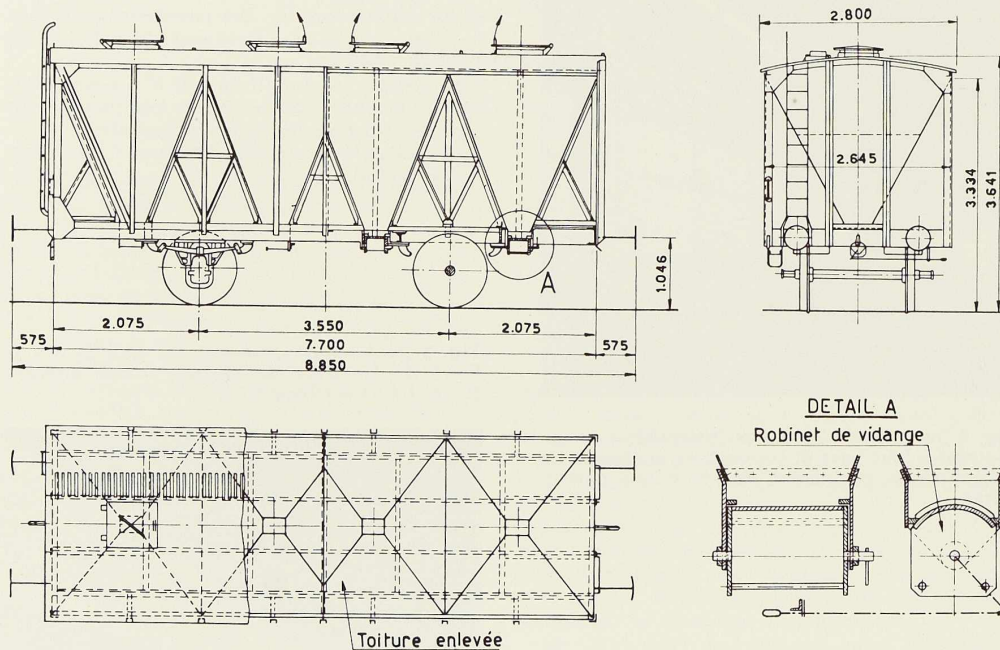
Elévation, vue en plan et coupe d'un wagon-trémie pour le transport du ciment en vrac, en service à la S. N. C. B.
